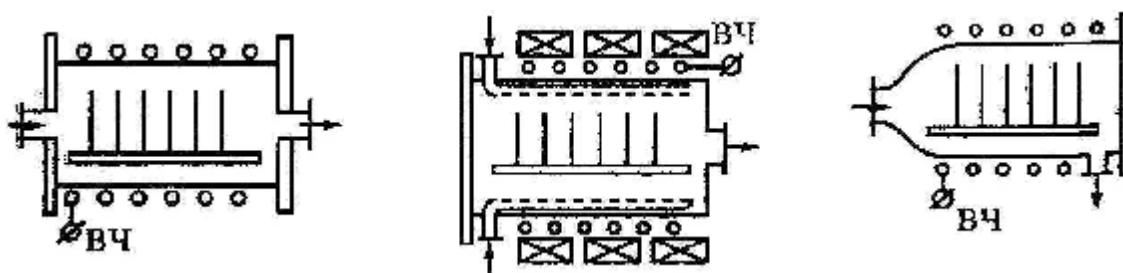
Схемы плазмохимических реакторов для обработки кремниевых пластин и изделий из пластмасс
